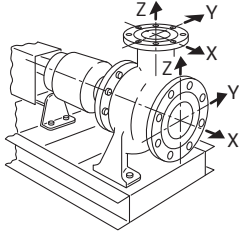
Pompa flanşlarında izin verilen kuvvetler ve momentler – EN-GJL-400-15 pik döküm pompa, 350 °C'ye kadar sıcaklıklar için
